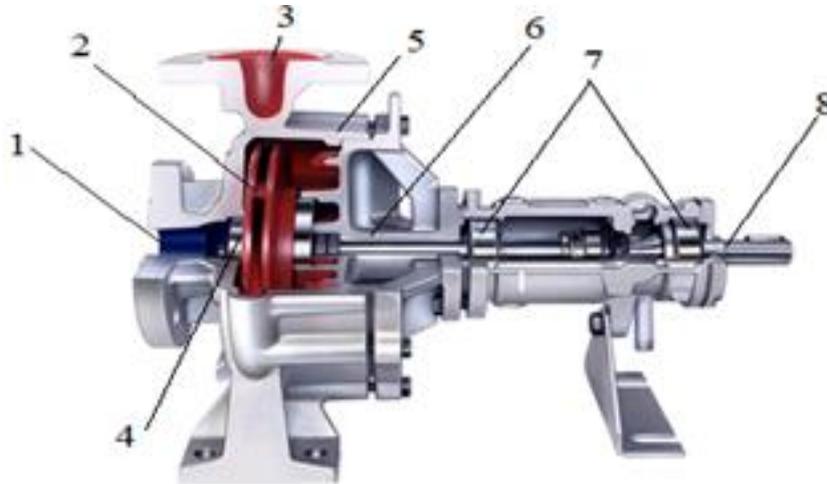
Схема устройства центробежного насоса: 1 – всасывающий патрубок; 2 – рабочее колесо; 3 – напорный патрубок; 4 – гайка крепления рабочего колеса на валу; 5 – корпус насоса; 6 – защитная втулка; 7 и 10 – подшипники; 8 – вал вращения.
